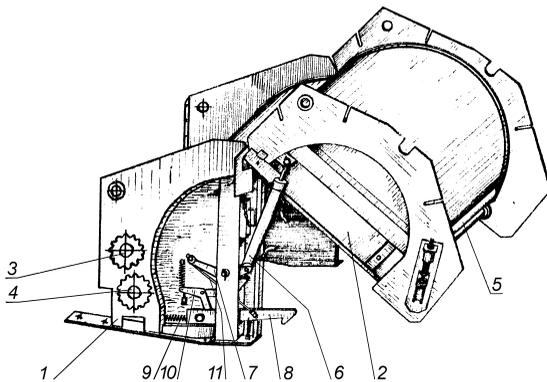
Камера прессования: 1 и 2 – передняя и задняя часть камеры; 3 – ведущий вал; 4 – верхний валец; 5 – ведомая ось прессующего механизма; 6 – гидроцилиндр; 7 – рычаг; 8 – защелка; 9 – пружина; 10 – рычаг; 11 – тяга
